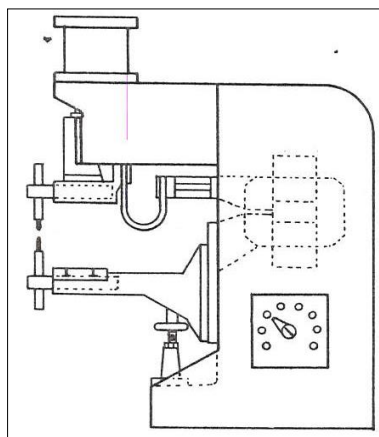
Máquina típica combinada para soldadura por puntos y por proyección.
